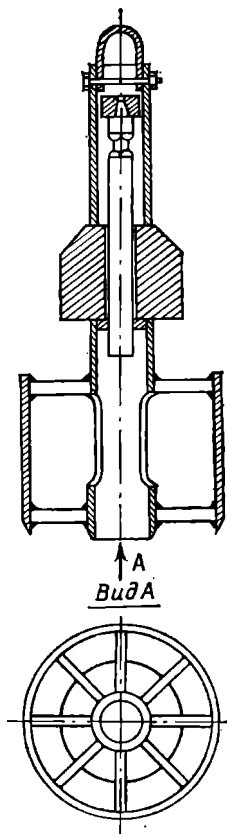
Забивной буровой снаряд конструкции Гидропроекта.
